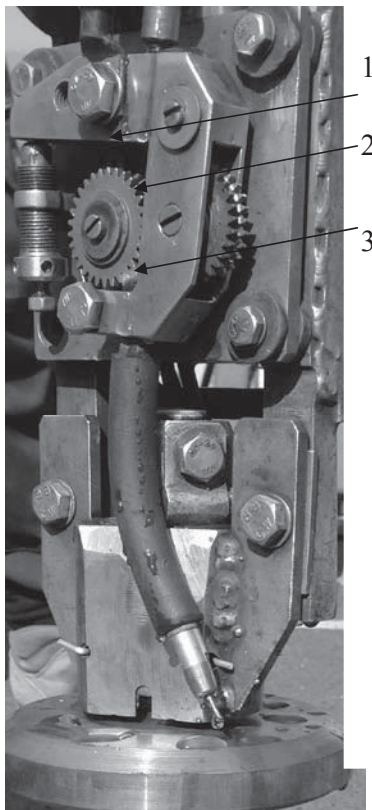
Сварочная горелка с колебателем: 1 — эксцентрично установленный подающий ролик; 2 — прижимной рычаг; 3 — колебатель
